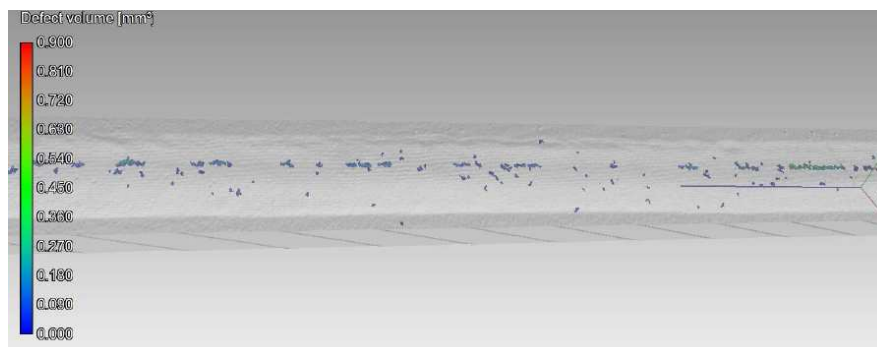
Bildabschnitt B (Schweißnahtmitte) aus Abbildung 54 – C.c.58.2
